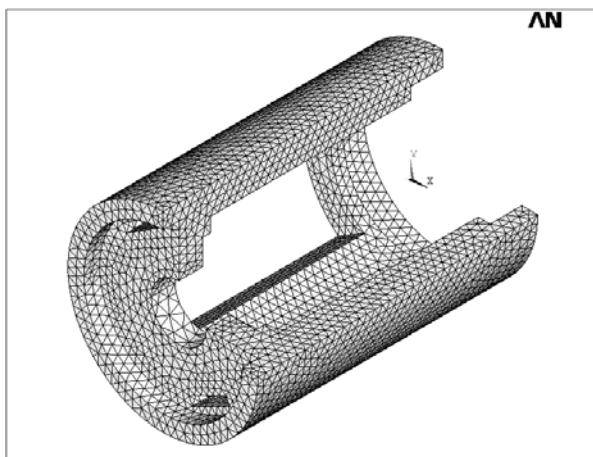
Конечно-элементная модель статора и корпуса насоса
